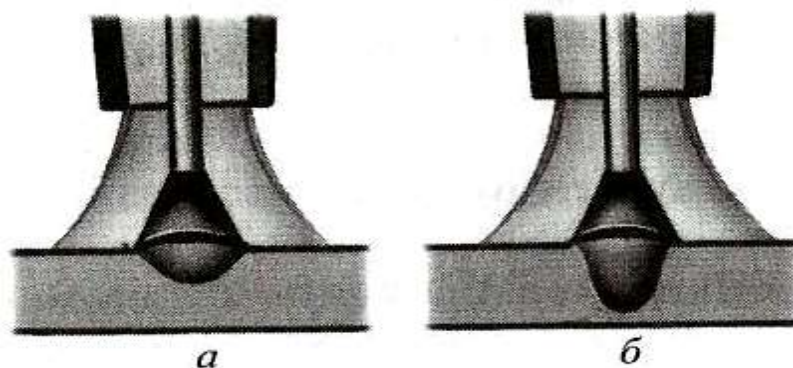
Влияние сварочного тока 100 А (а) и 200А (б) на глубину проплавления
